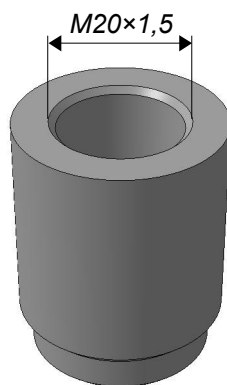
Бобышка сварная для крепежа преобразователя ПД-1Ц
